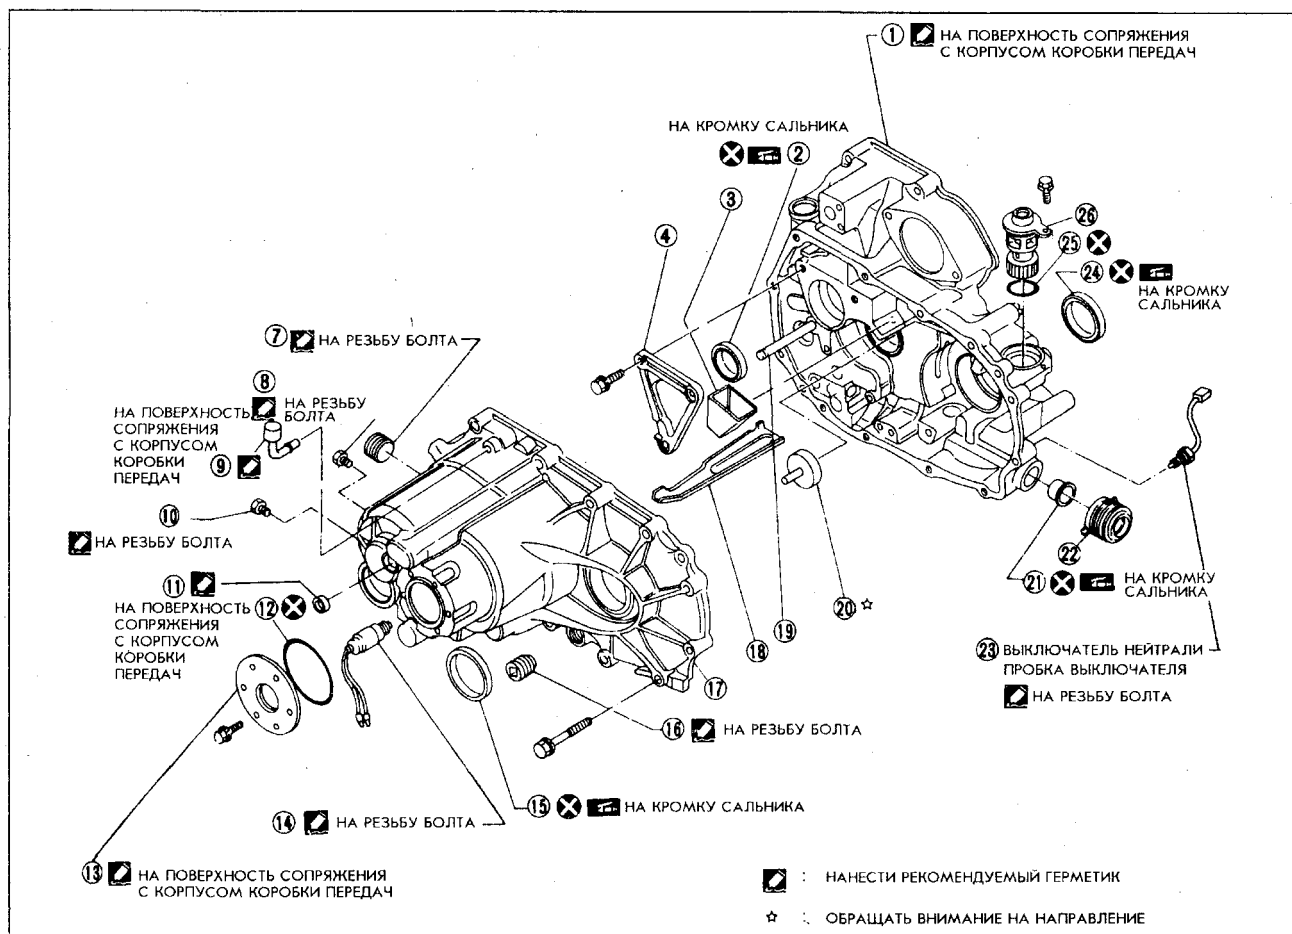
Компоненты корпуса коробки передач RS5F31A.
